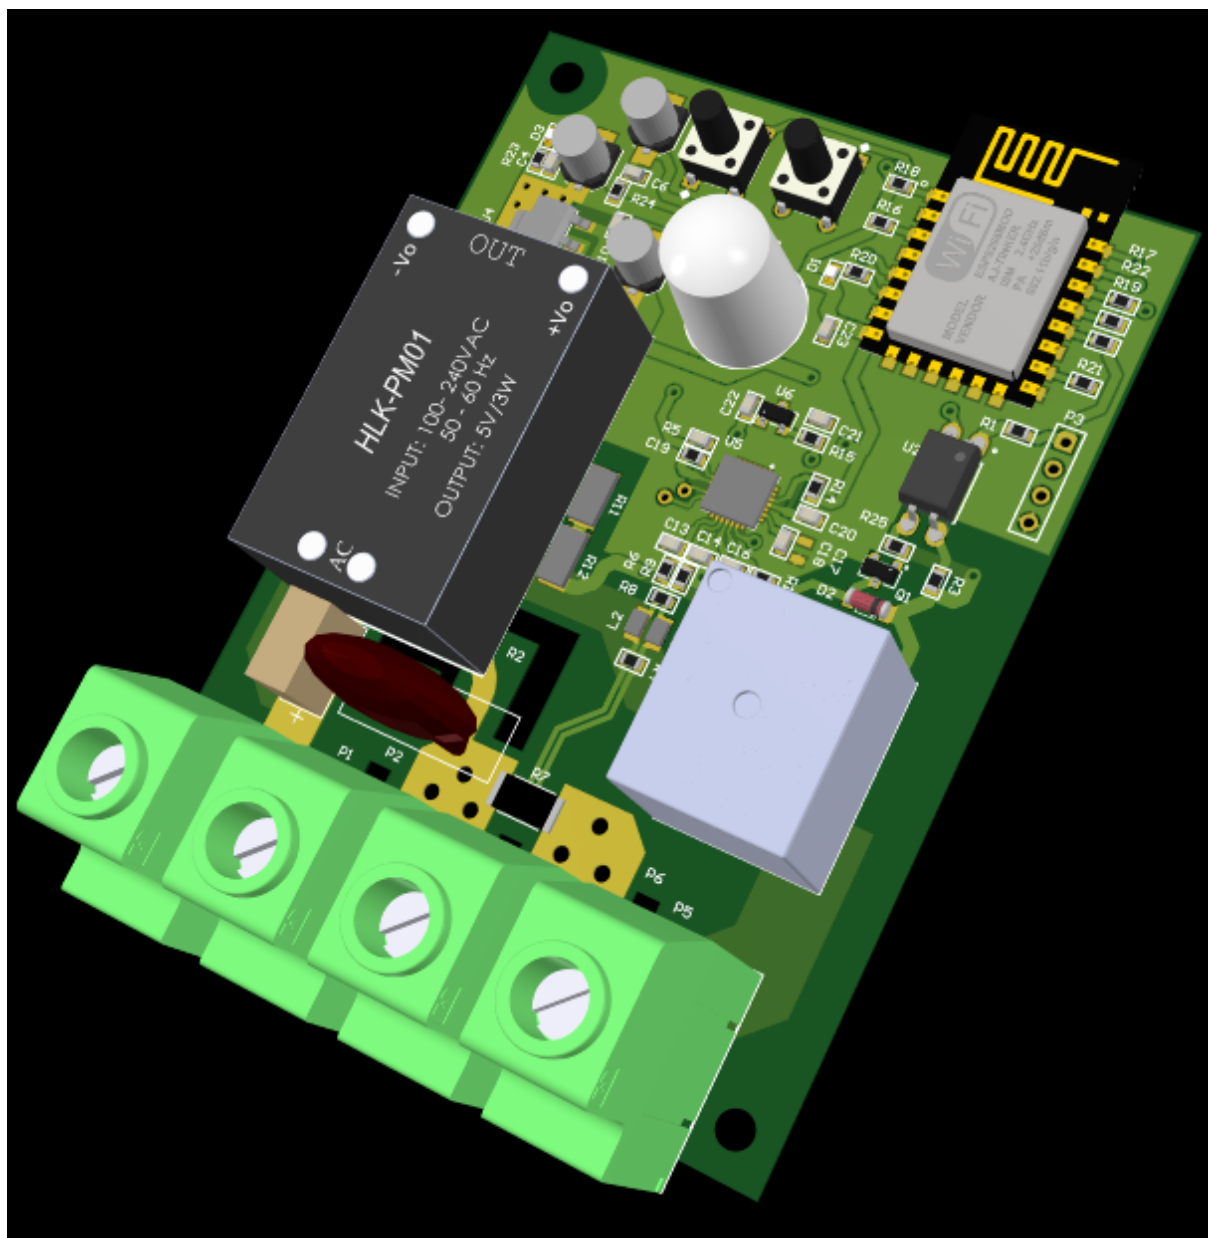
Visão isométrica da representação 3D do *layout* da PCB.
